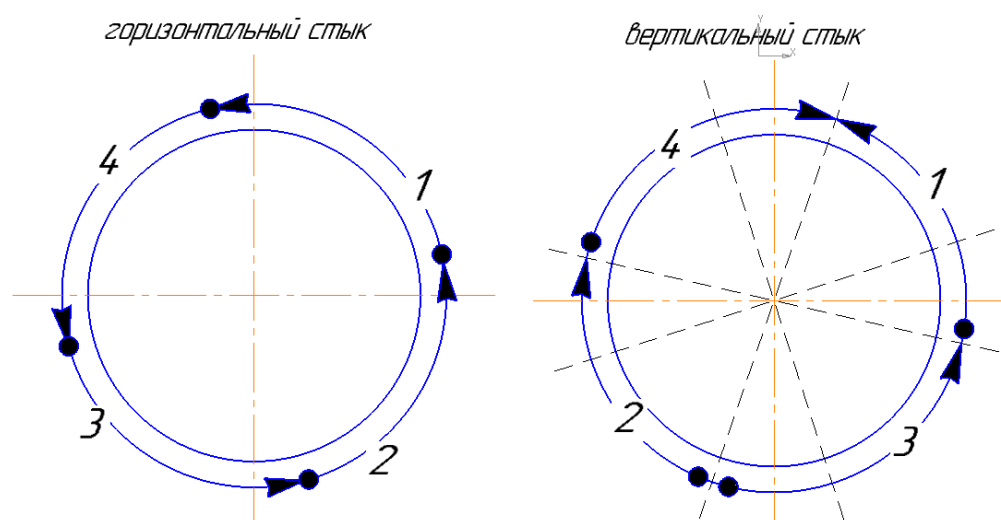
Последовательность сварки корневого слоя шва
